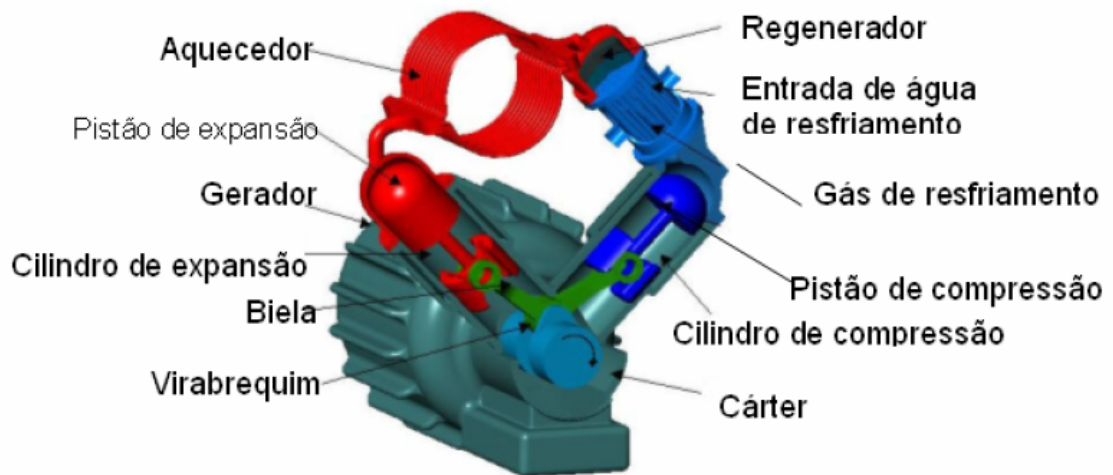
Motor Stirling Solo 161, detalhamento de principais partes.
